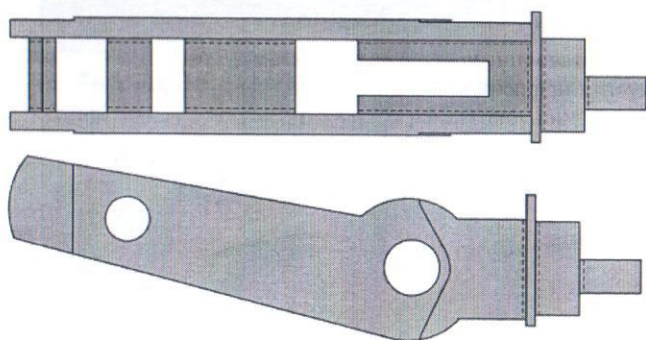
Контроль околошовных зон сварных соединений деталей рычага
